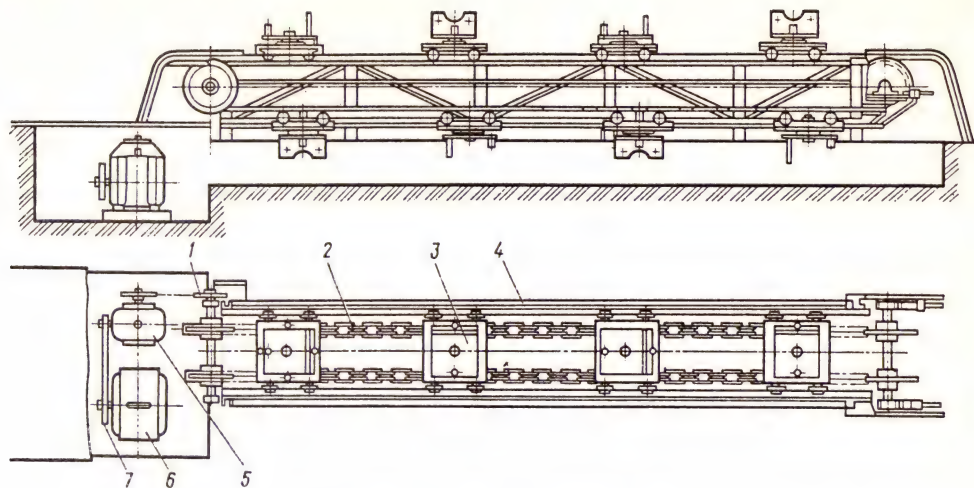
Вертикально замкнутый конвейер для сборки коробок передач
